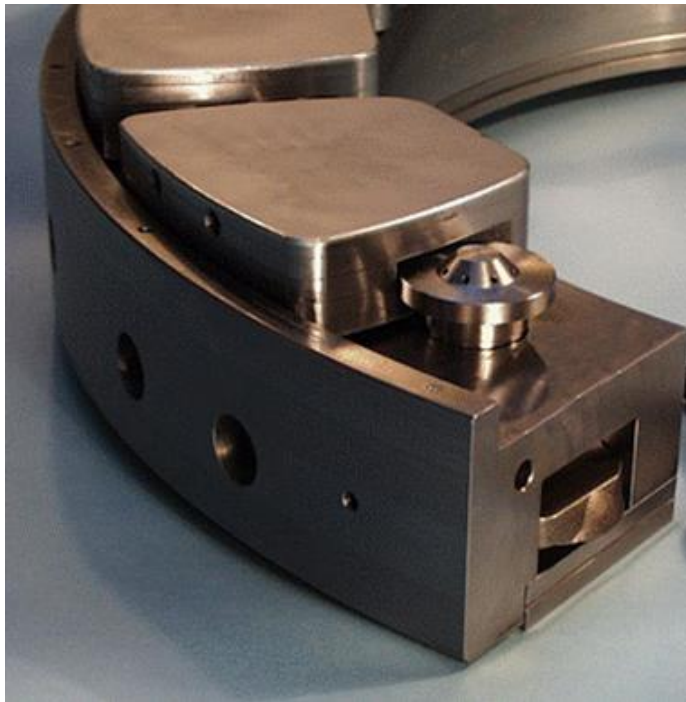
Упорный подшипник с «направленной смазкой» (Waukesha Bearings, Великобритания)
